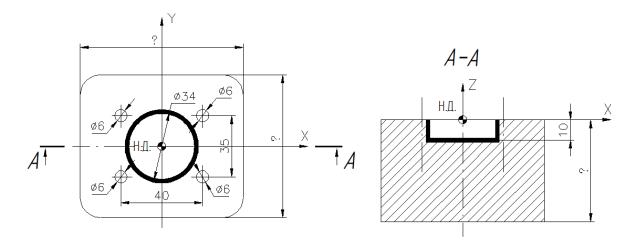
Операционный эскиз обрабатываемой детали
